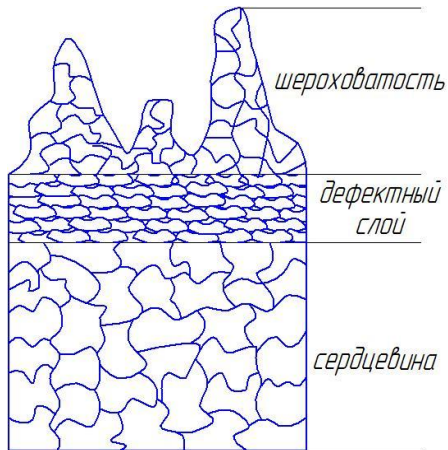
Схематичний вигляд ділянки поверхневого шару
